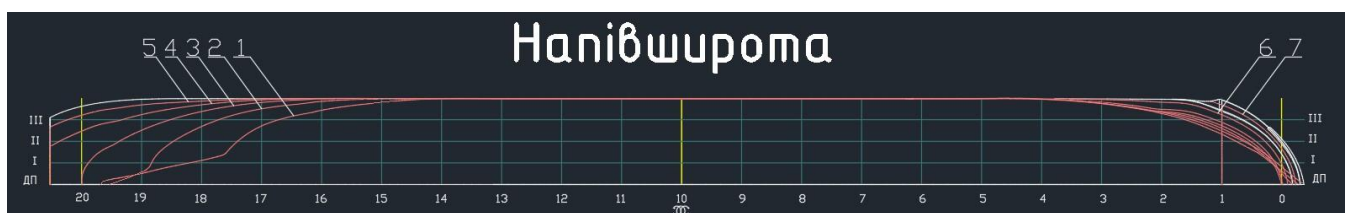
Створена 3D модель теоретичної поверхні корпусу балкера
